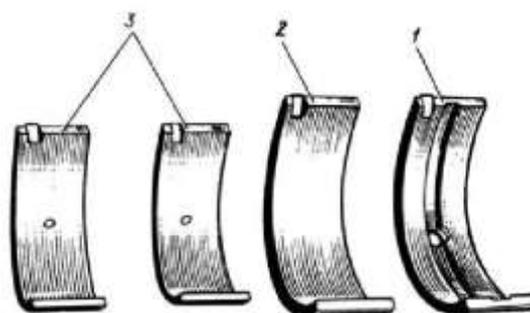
Вкладыши подшипников коленчатого вала:
